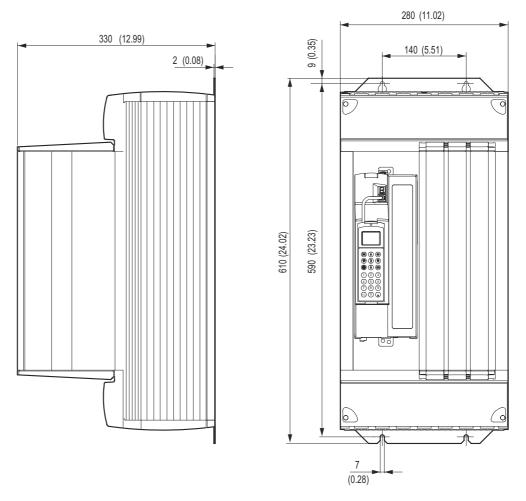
Dimensões MDX61B, tamanho 5, dimensões em mm (in)
